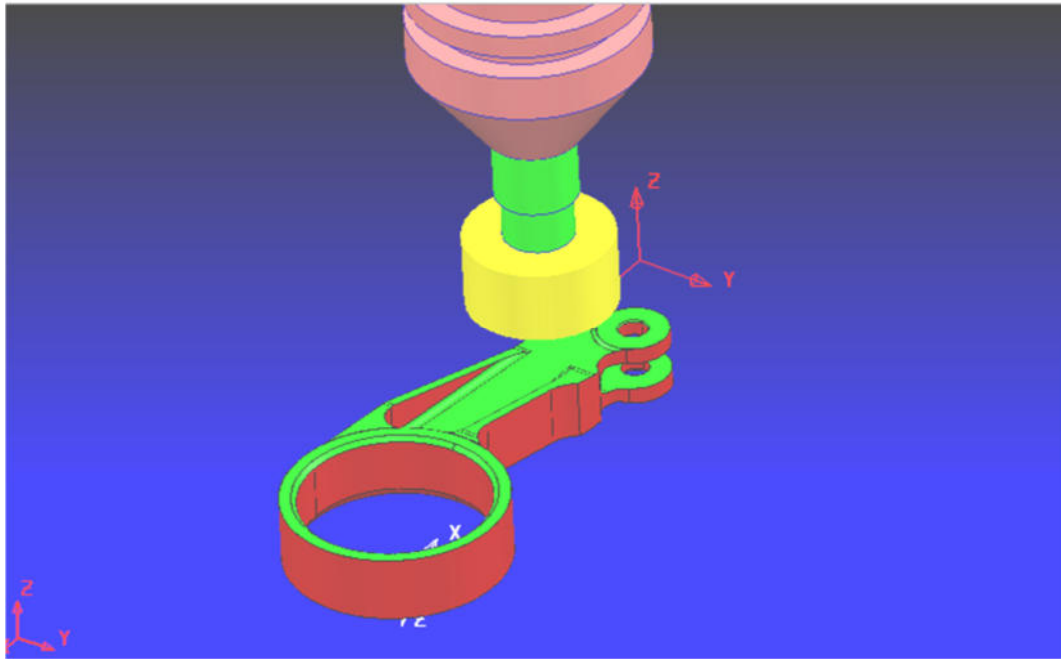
Фрезерування торцевою фрезою поверхні - 2,
